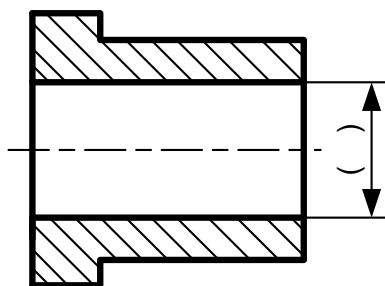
Обозначения обработки под отверстия в сборочном чертеже
